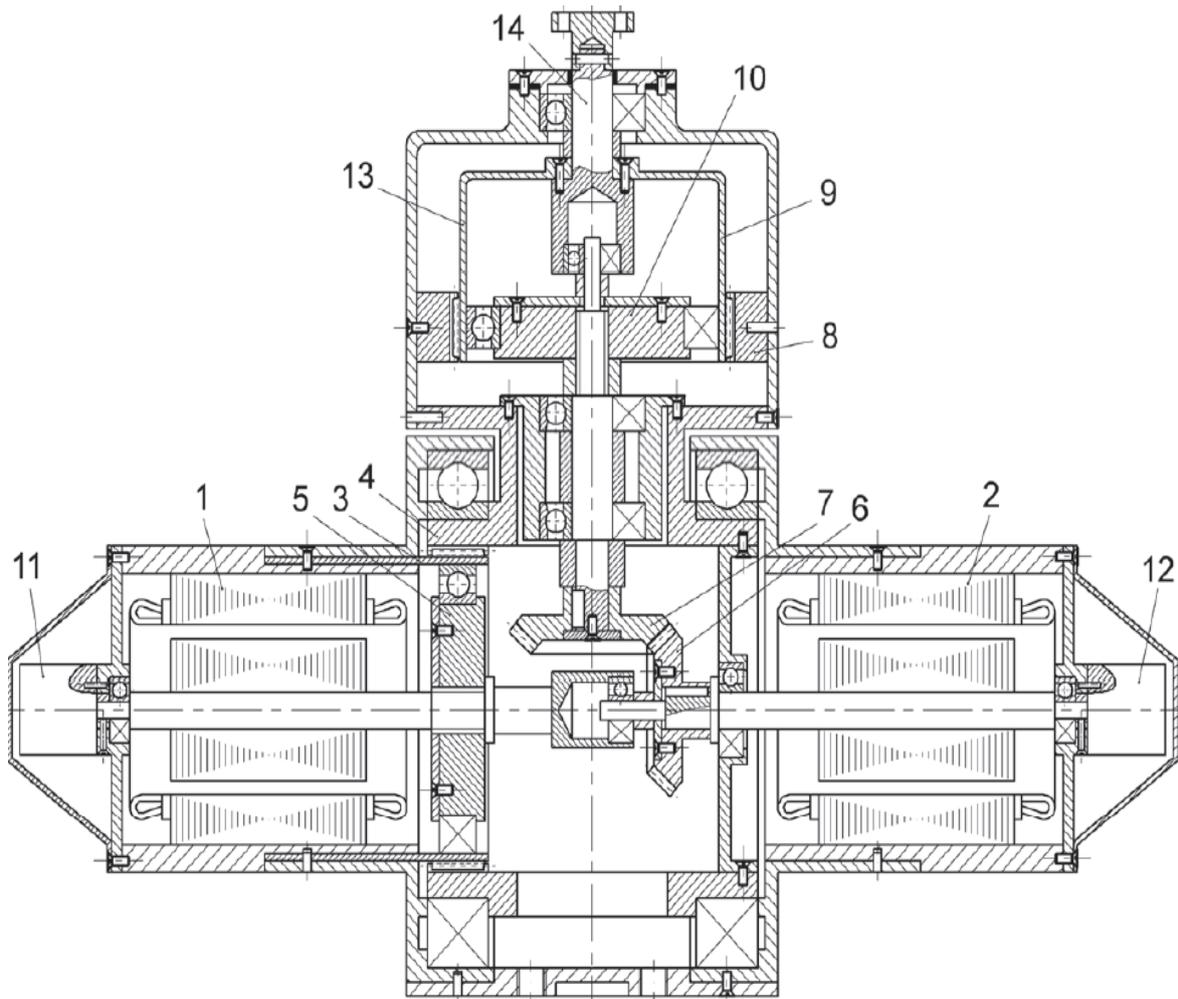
Двухкоординатный мехатронный модуль движения
